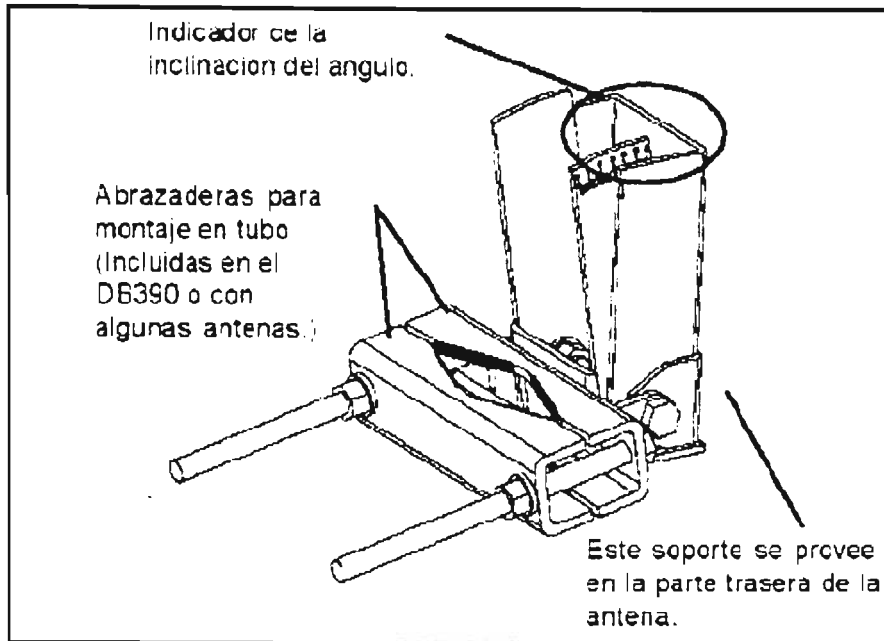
Parte inferior del DB5098 ensamblado al tubo.
